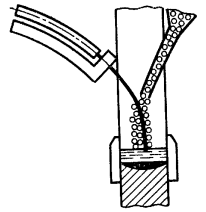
Схема сварки с присадкой дополнительного материала в виде металлической «крошки»
